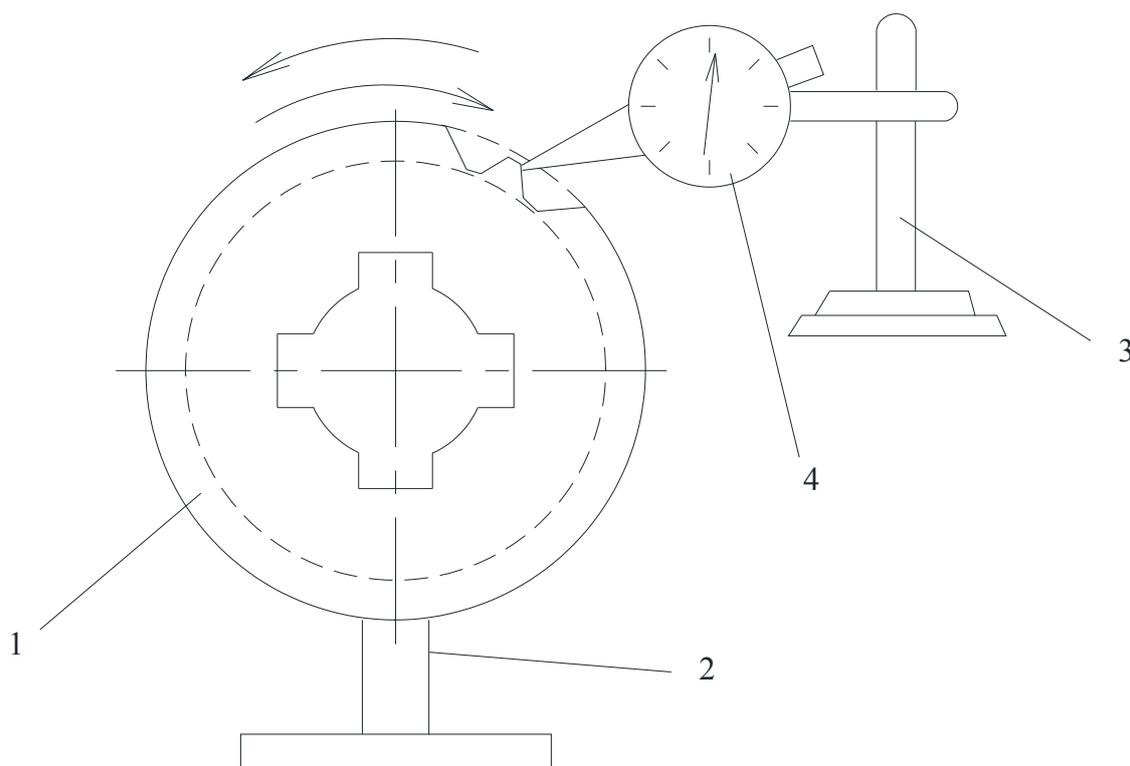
Схема контроля бокового качания колеса на валу: 1 – зубчатое колесо; 2 – стойка с втулкой; 3 – штатив; 4 – индикатор
